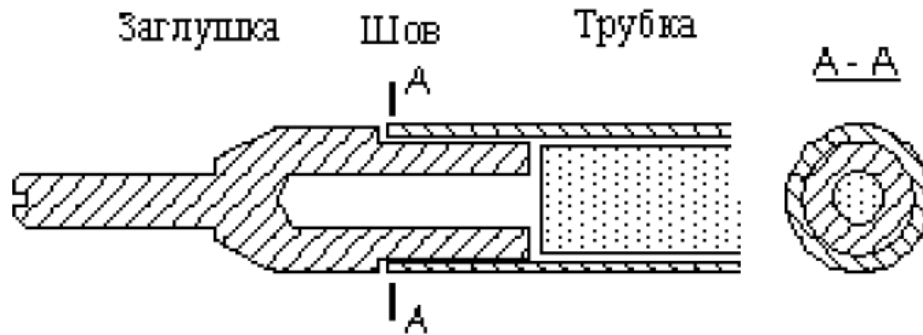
Вид сварного шва твэла ВВЭР
